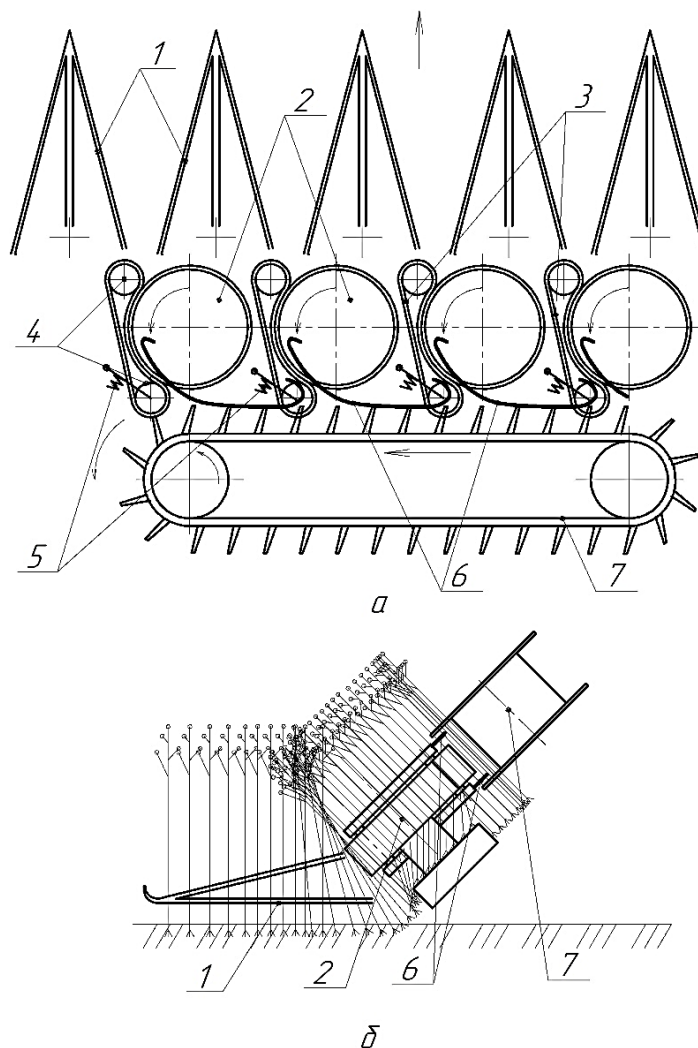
Дисково-пасовий льонобральний апарат (а – вид зверху, б – вид збоку): 1 – подільники; 2 - бральні диски; 3 - бральні паси; 4 – ролики; 5 - підпружинені кріплення; 6 - напрямні прутки; 7 - поперечний транспортер
